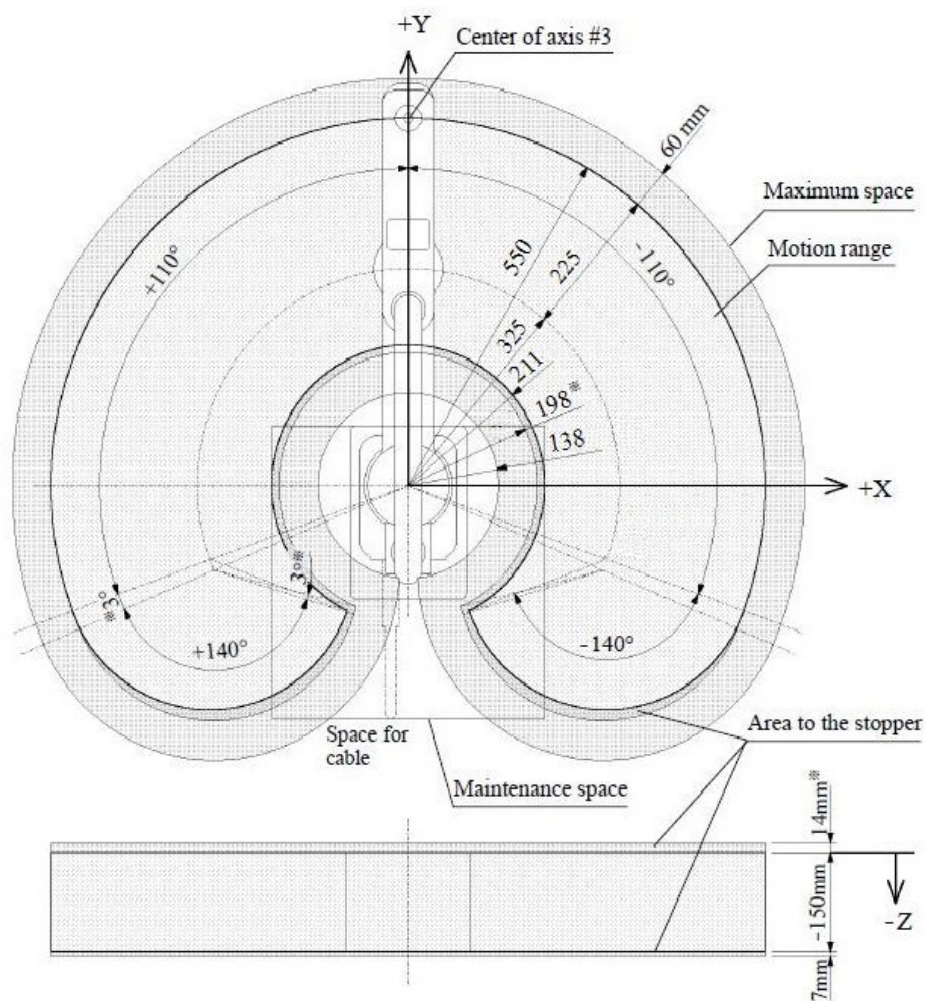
Rozměry manipulátoru (mm) [11].
